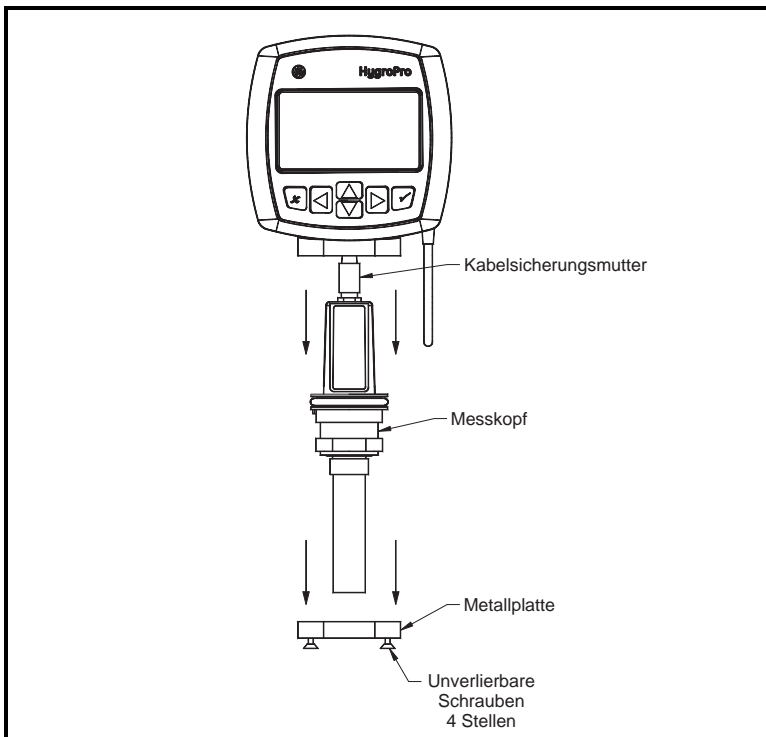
Entfernen des Messkopfs vom Messwandler
